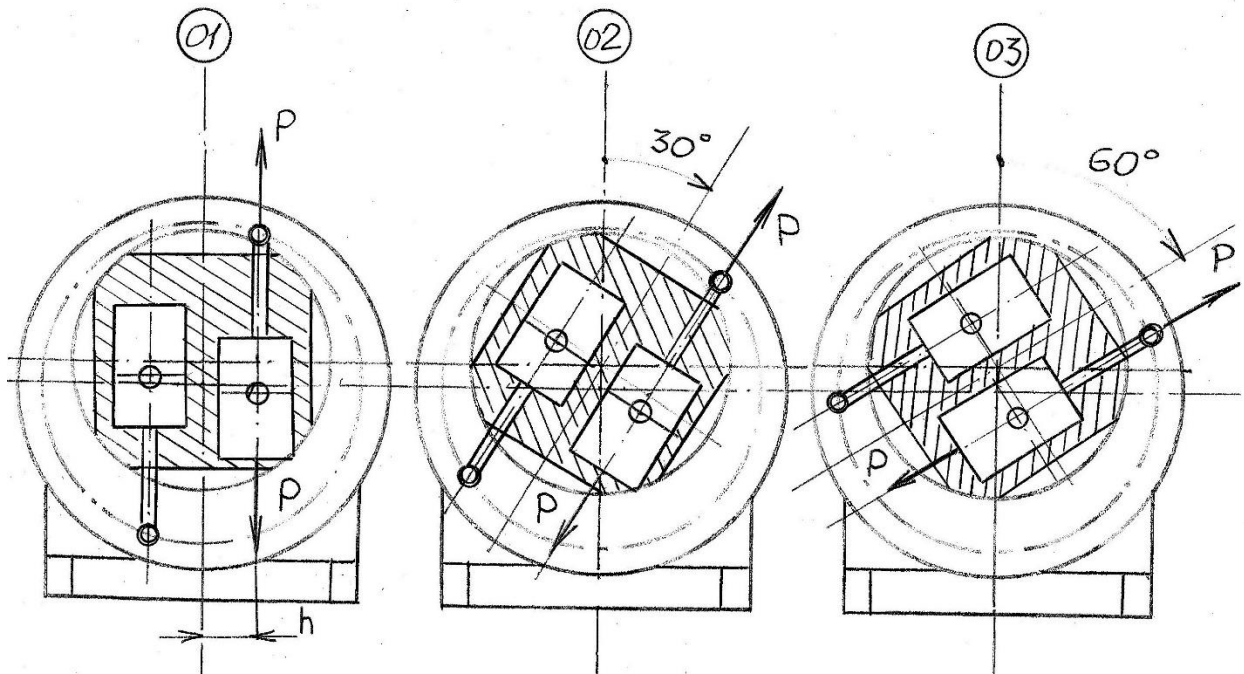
Чертёж позиций поршней и цилиндров роторного двигателя в процессе вращения
